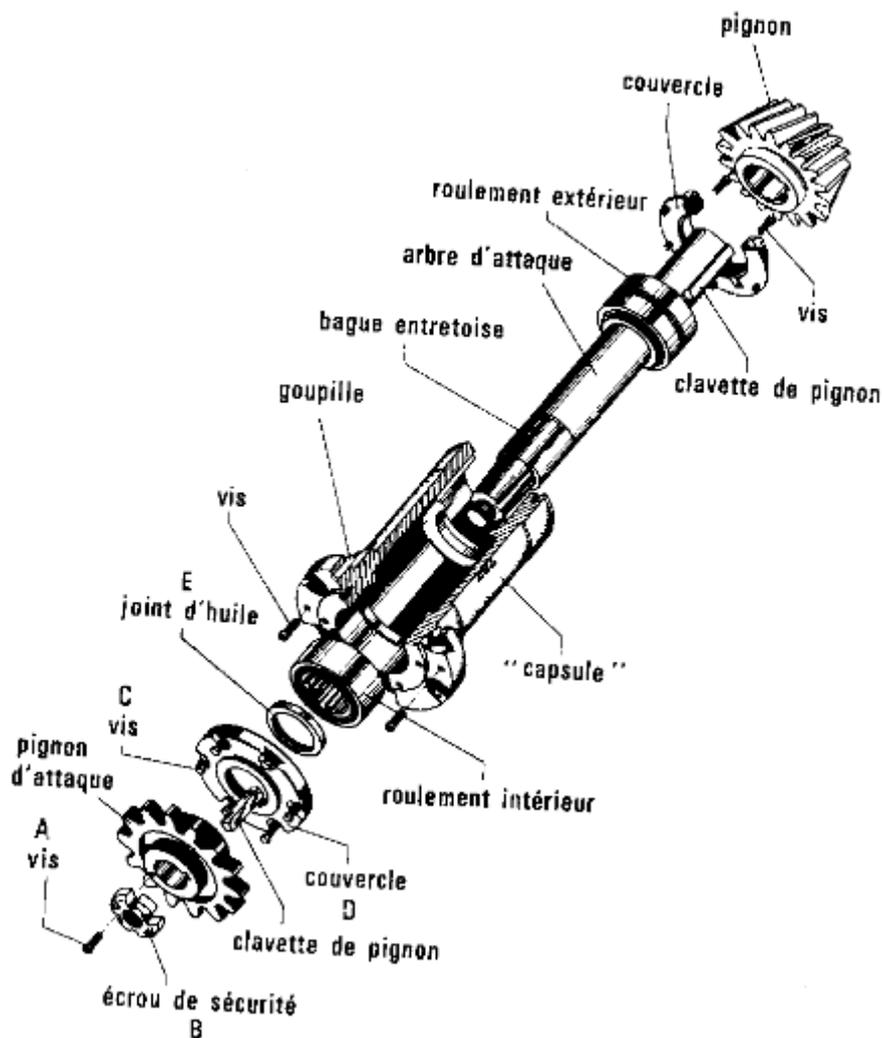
Vue éclatée de l'arbre d'entraînement [1]
